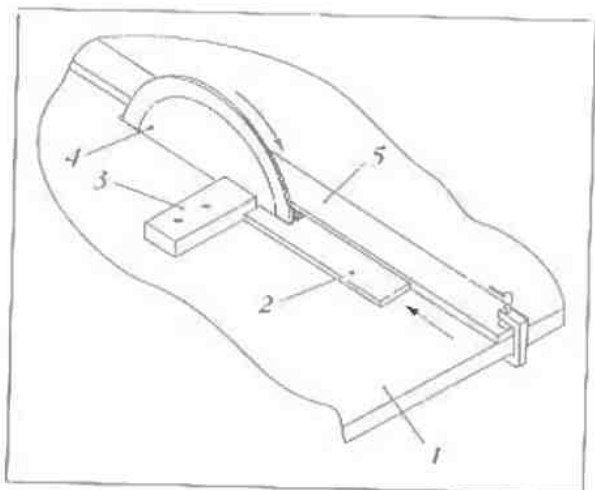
Нарезание зубьев гребня на циркулярной пиле: 1 – рабочий стол; 2 – заготовка; 3 – упор; 4 – фреза; 5 – направляющая линейка
